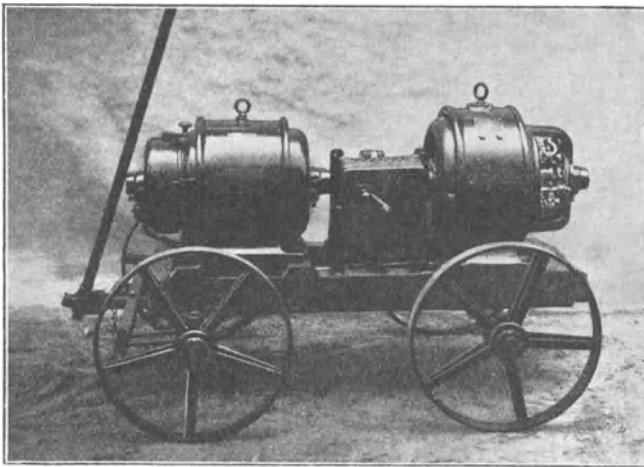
Fahrbarer Gleichstromschweißumformer.
